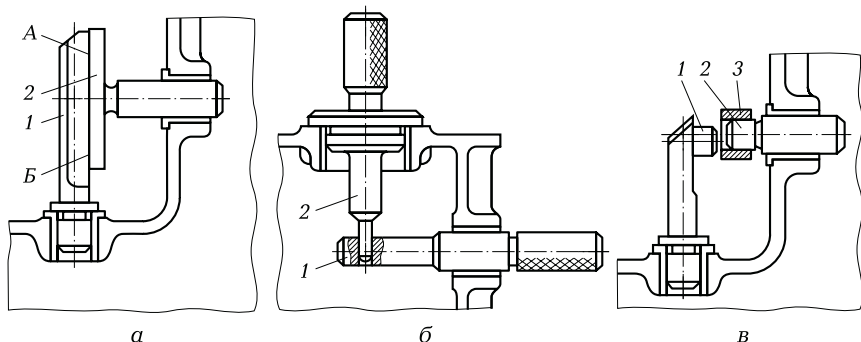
Схемы контроля взаимного расположения осей в корпусе редуктора конической зубчатой передачи:
